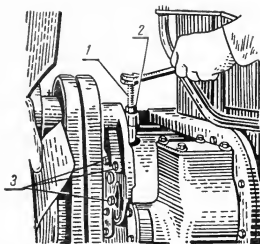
Регулировка натяжения ремней вентилятора двигателей КДМ-46 и КДМ-100:
